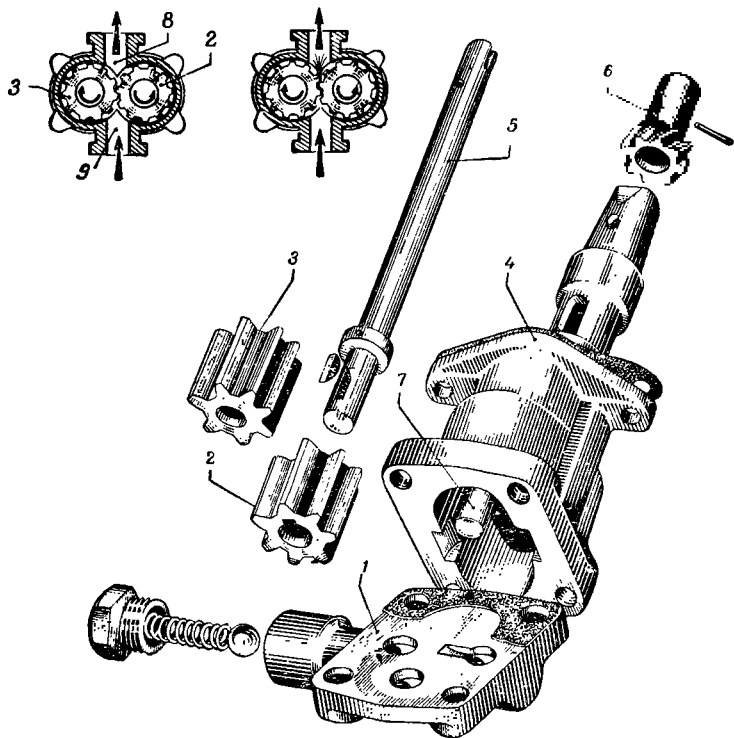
Схема работы (вверху) и детали (внизу) масляного насоса двигателя ГАЗ-51.
